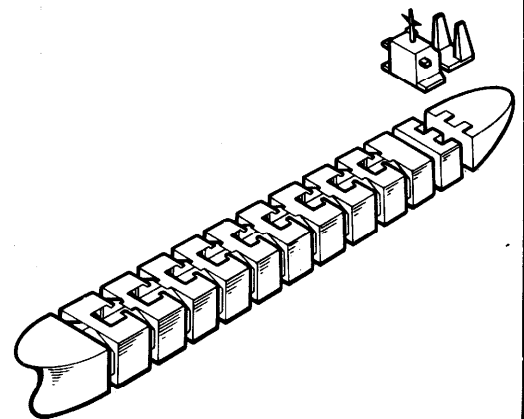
Схема разбивки корпуса судна типа „Борис Бутoma“ на блоки
